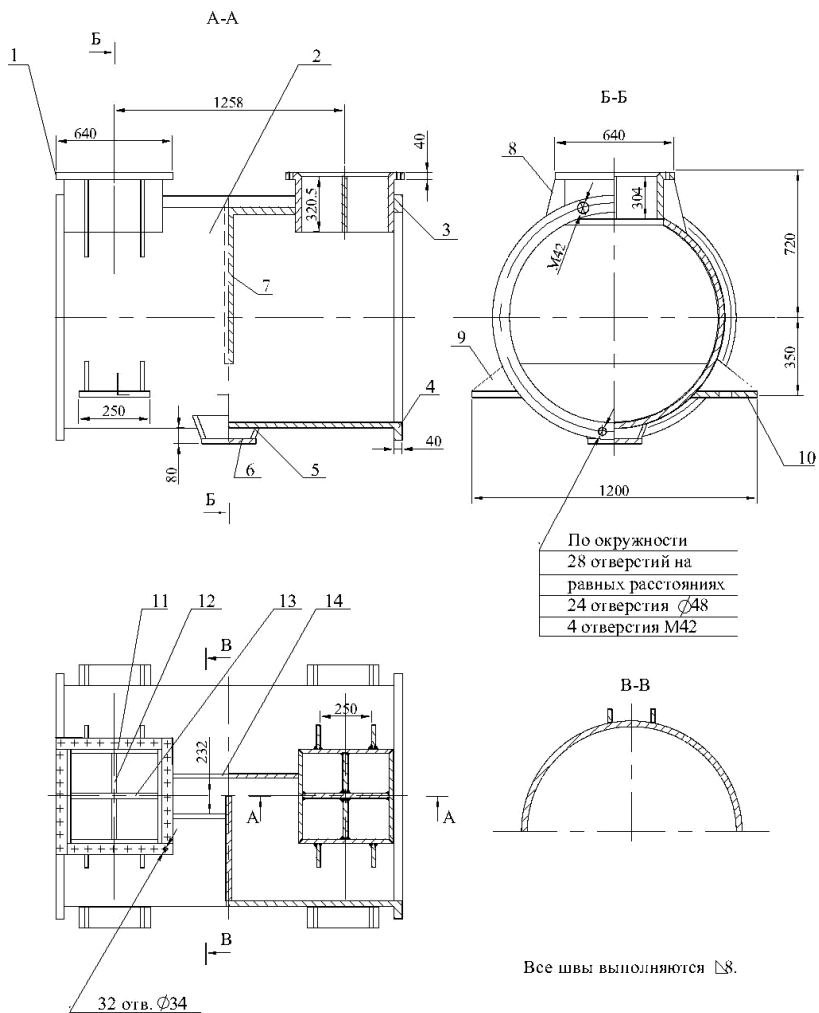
Корпус воздухоохлаждителя турбокомпрессорной установки:
